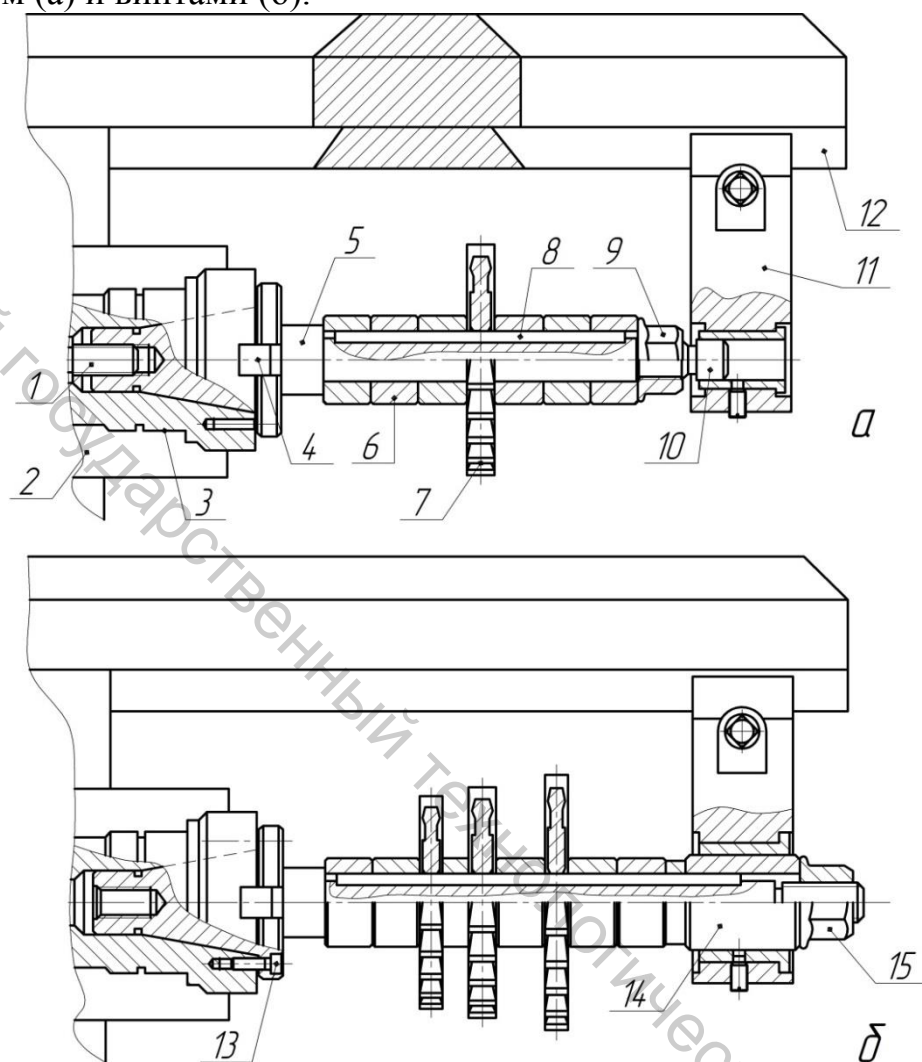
Оправки двухопорного крепления с цилиндрической цапфой (а) и поддерживающей втулкой (б) к горизонтально-фрезерным станкам:
